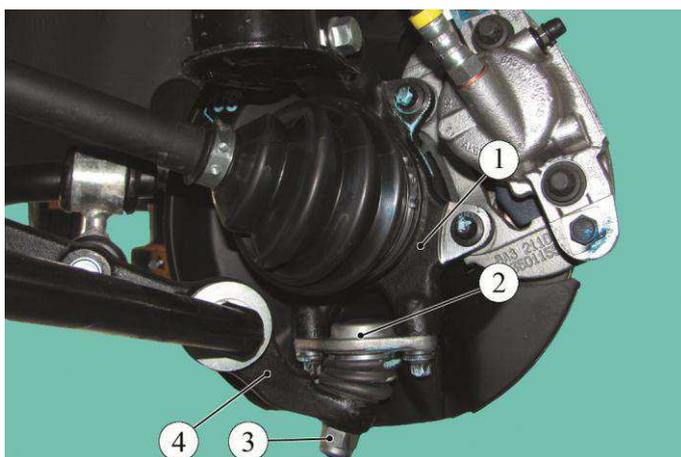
Выпрессовка шарового пальца крепления поворотного кулака к нижнему рычагу передней подвески:
